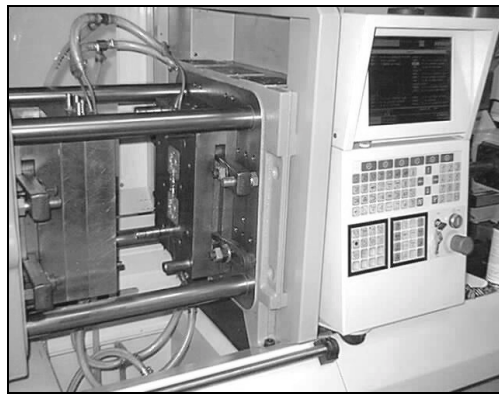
Molde com insertos de estereolitografia na máquina injetora
